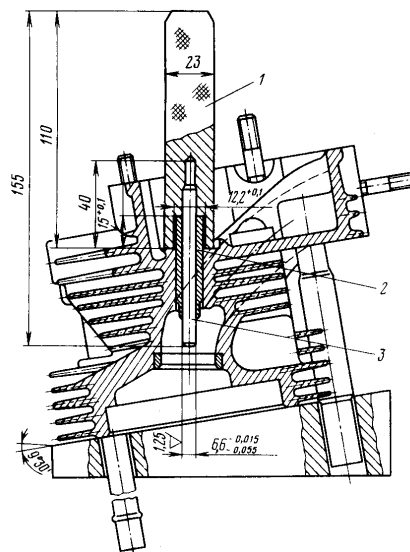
Оправка для запрессовки направляющих втулок клапанов:
